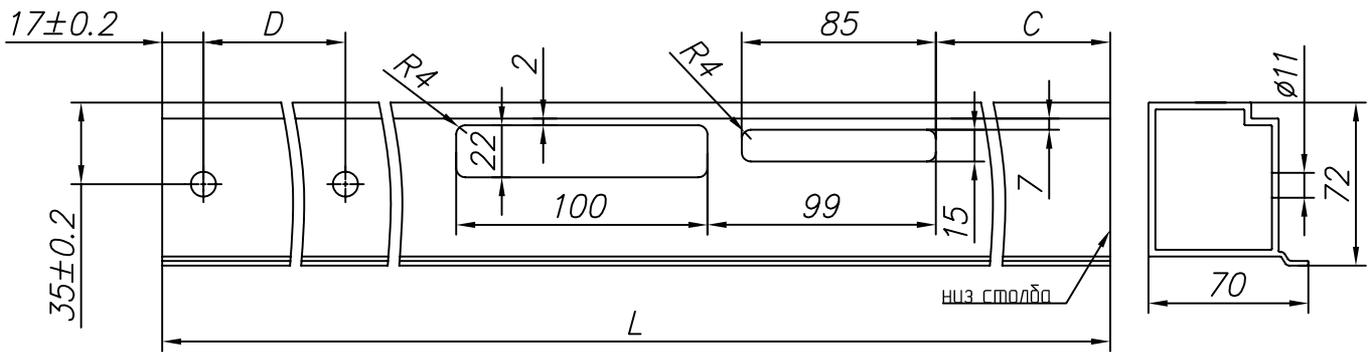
Изготовление столба притвора с пазом для автоматической защелки для калитки с левым открыванием (защелка 118WE)
